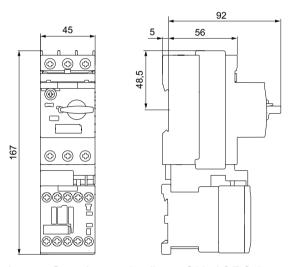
Arrancador directo S00, AC/DC, bornes de tornillo 3RA2110-..A
